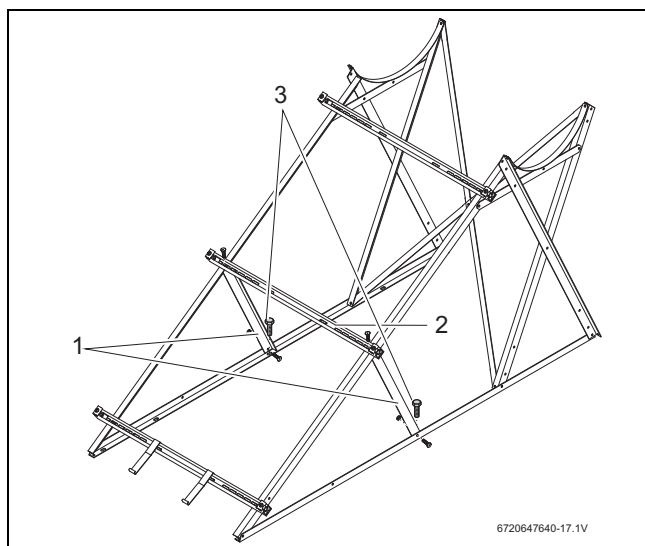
Apoyos adicionales para sistema de cubierta plana (sistema de 150/200 I)
